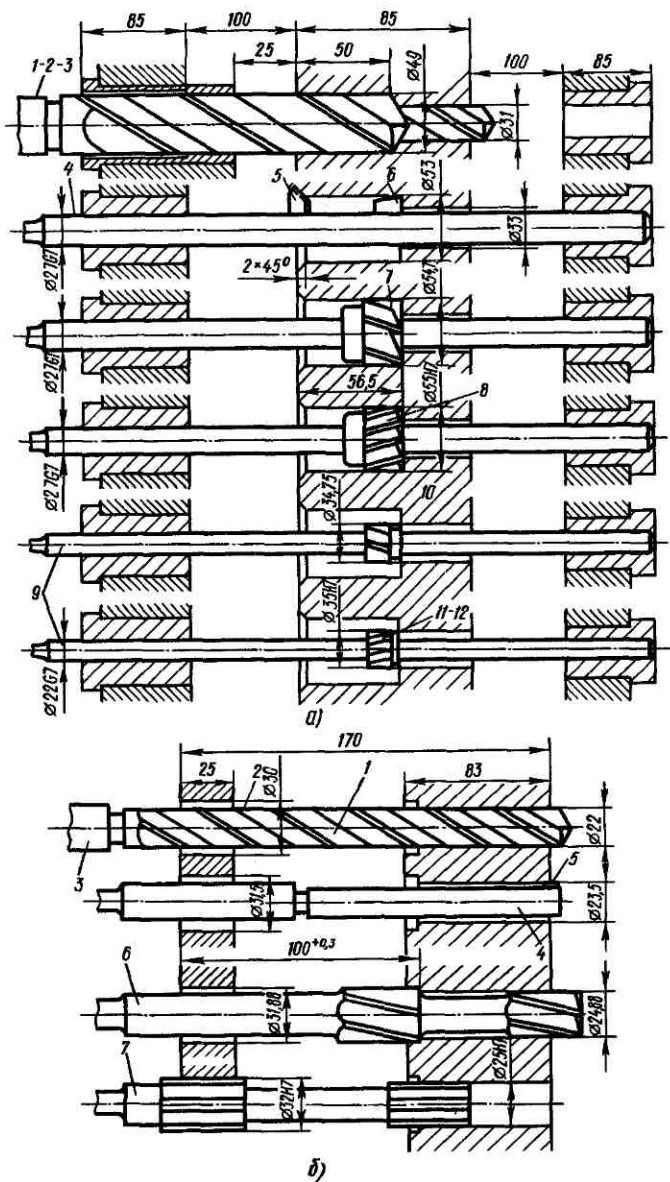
Обработка отверстий $\varnothing 55H7$, $35H7$ с фаской
